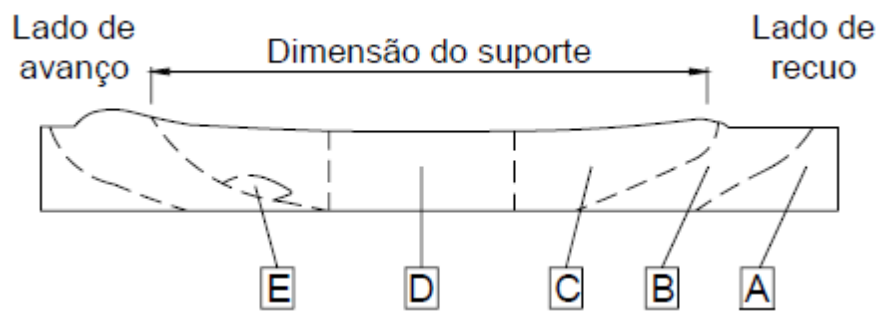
Seção transversal de regiões de uma união soldada pelo processo FSW [12].
